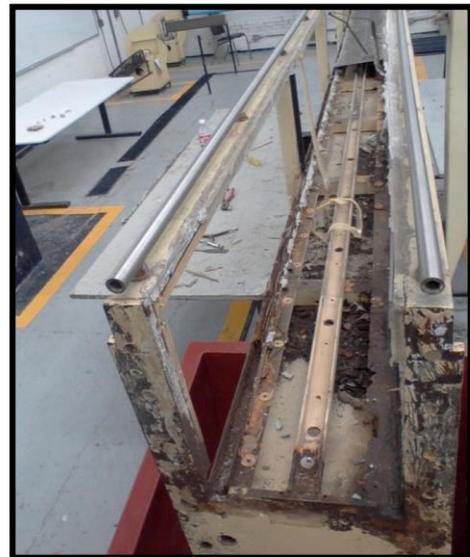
Sección L con las paredes laterales retiradas y en proceso de remover la plantilla.
